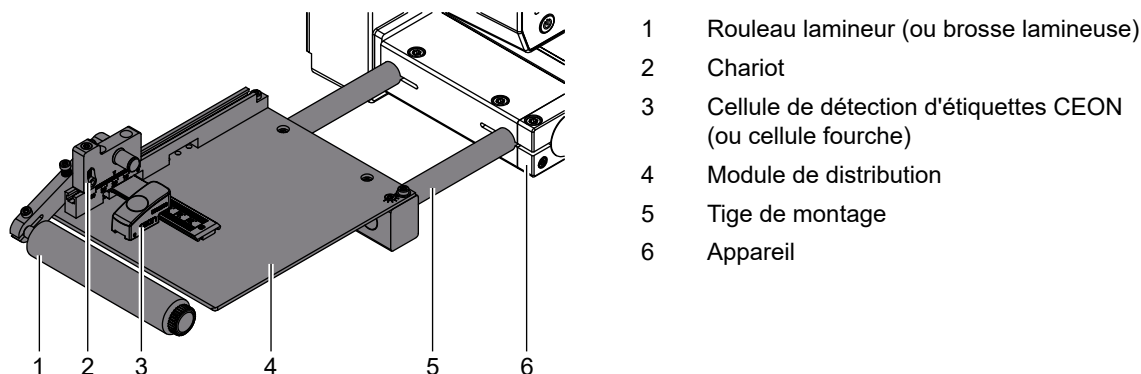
Vue d'ensemble module d'étiquetage, exemple
